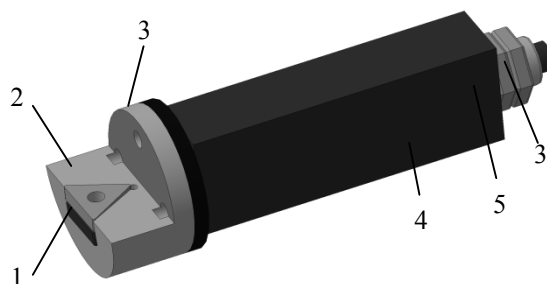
3D модель безвершинного резца для косоугольного резания: 1 – СМП, 2 – сменная опорная часть, 3 - поворотная часть, 4 – державка, 5 – гайка
